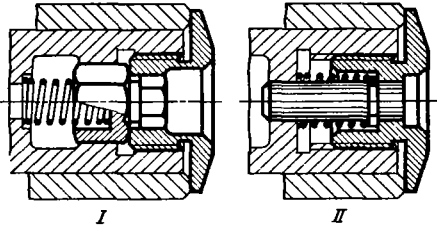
Стопорение гаек пружинным фиксатором: I — для гаек с внутренним шестигранником; II — для гаек с внутренними треугольными шлицами
